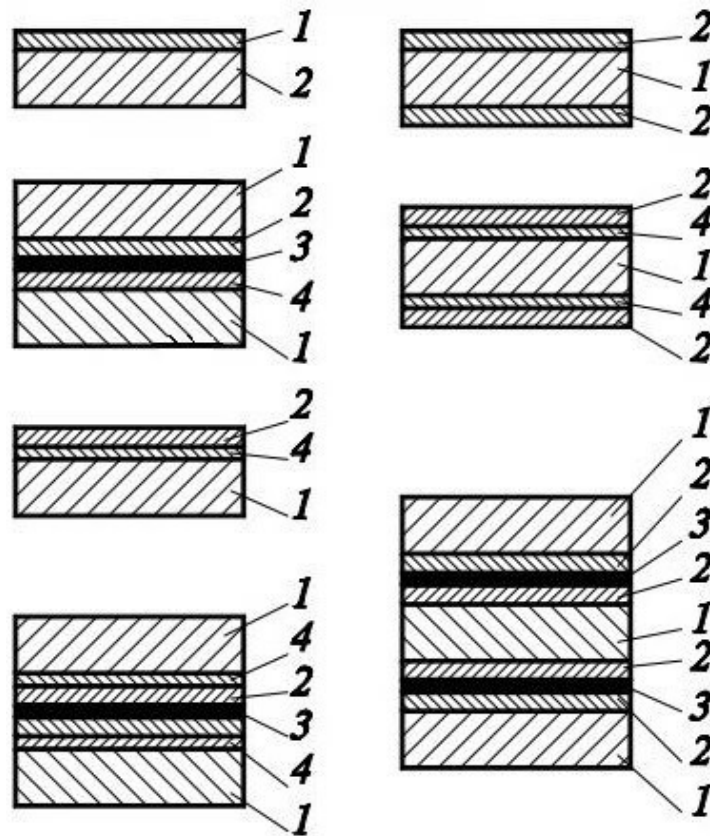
Схеми укладання біметалів у пакети перед спільною прокаткою: 1-основний шар, 2-плакуючий шар, 3-роздільний підшар, 4-з'єднувальний підшар
